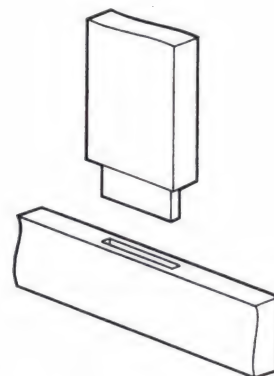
Схема изготовления шипа для соединения паз и шип.
